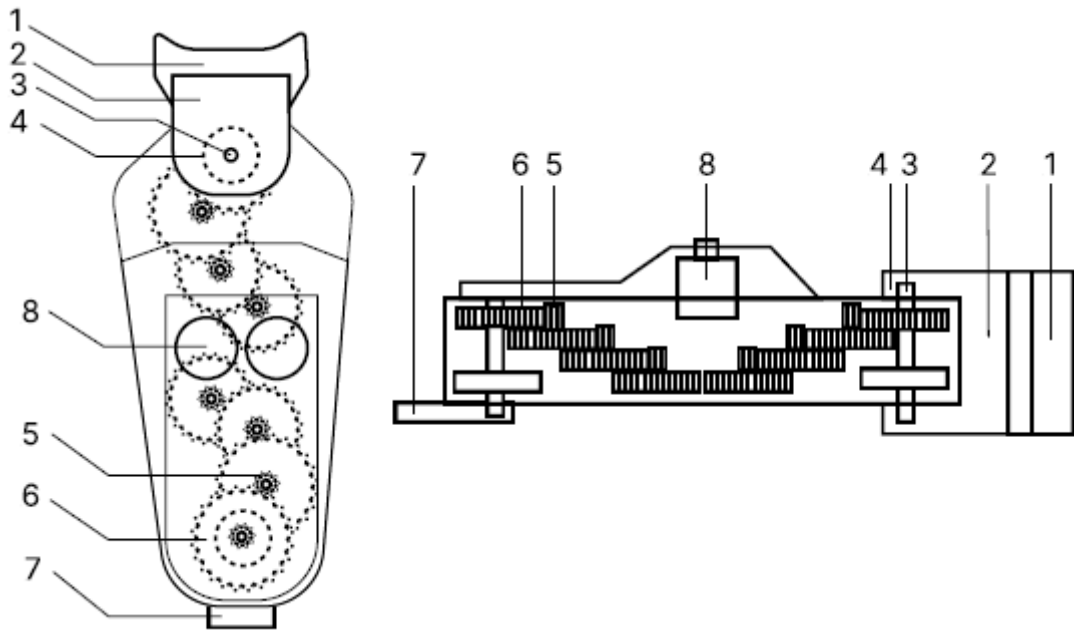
зпроектований аналог п'ястної кістки: 1 – фіксатор сконструйованої основної фаланги, суглобова поверхня; 2 – фаланговий суглоб; 3 – вал; 4 – потенціометр; 5 – шестерня мала; 6 – шестерня велика; 7 – фіксатор штучної п'ястної кістки; 8 – приводи.
